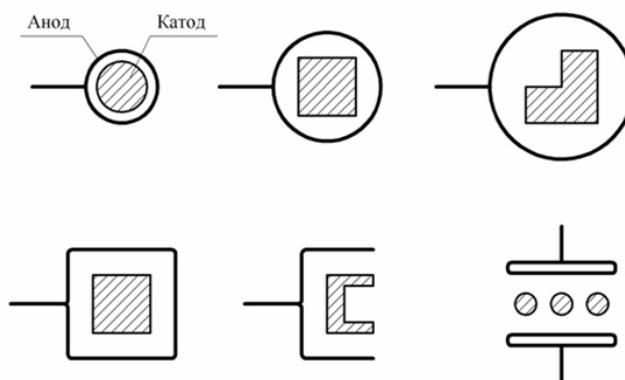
Різновиди форм анодів тліючого розряду залежно від форми перерізу зварюваних деталей
